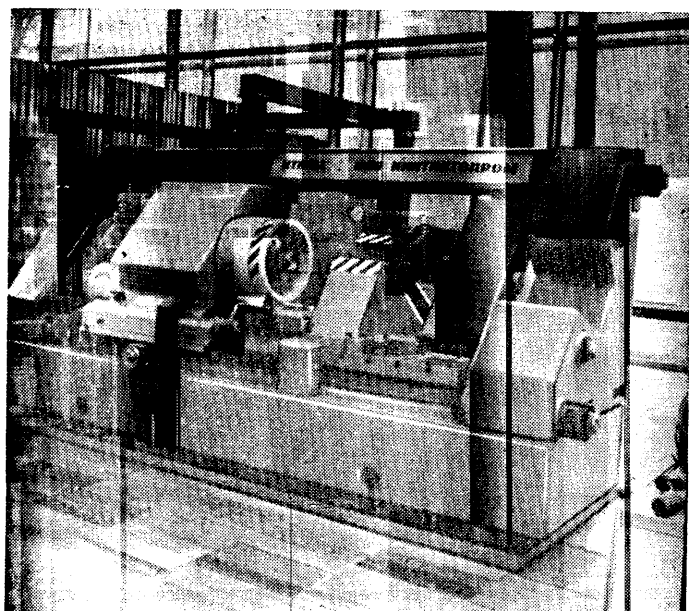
Машина для сварки трением мод. ПСТ-60
